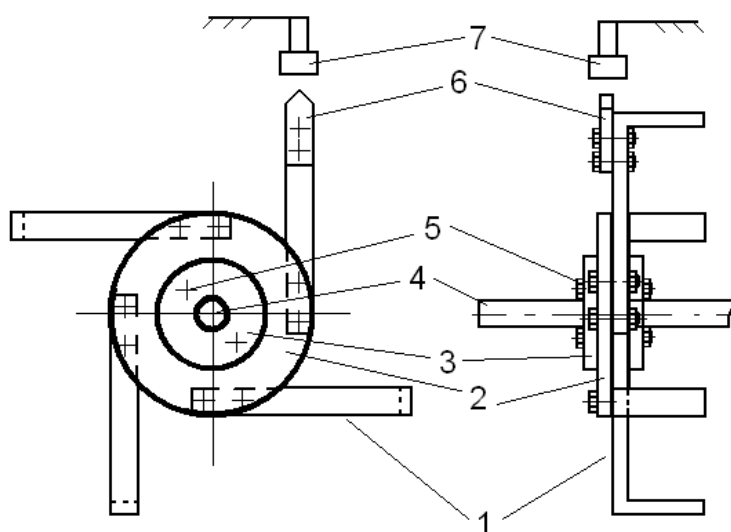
Схема устройства секции почвообрабатывающей фрезы
